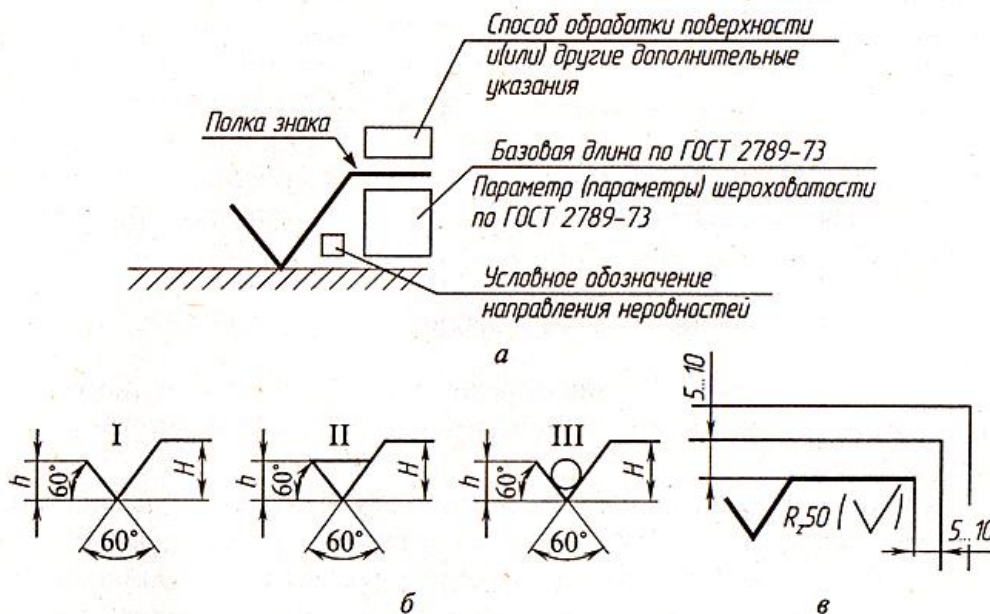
Обозначение шероховатости: а – размещение дополнительной информации; б – размеры условного знака; в – общий знак шероховатости ставится в правом верхнем углу чертежа
